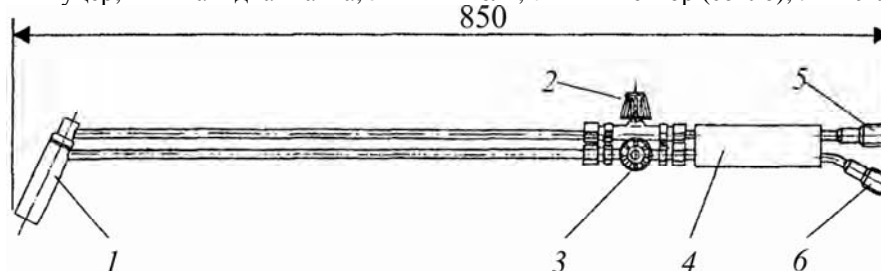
Горелка ПВ-1: 1 — головка горелки; 2 — вентиль подачи воздуха; 3 — вентиль подачи горючего; 4 — державка; 5 — штуцер воздуха М 16×1,5; 6 — штуцер горючего М 16×1,5 Н
